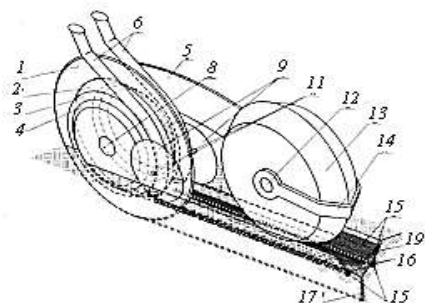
Технологическая схема работы комбинированного однодискового сошника с двухсторонними ребрами и прикатывающим катком: 1 – плоский диск; 2, 4 – реборды; 3 – бороздкообразователь; 5 – корпус; 6 – семянаправитель; 8, 11, 12 – оси; 9 – сферический диск; 13 – прикатывающий каток; 14 – чистик; 15 – ложа; 16 – семена; 17 – щель; 19 – бороздка
